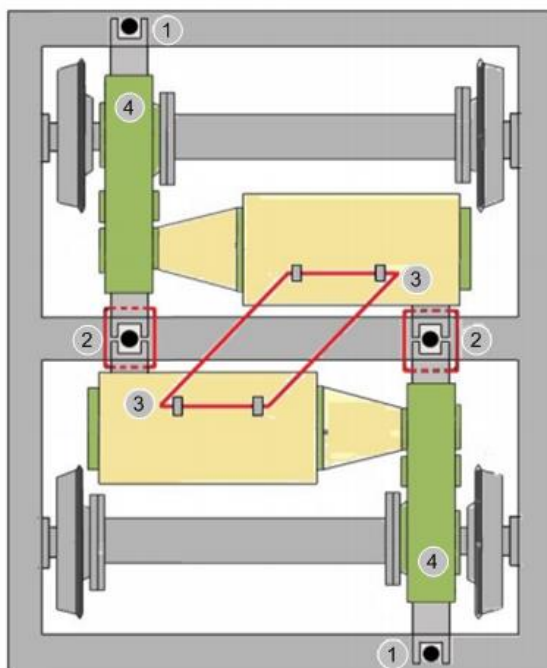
Схема кріплення тягового редуктора: 1 – кріплення через гумометалевий шарнір до кінцевої поперечної балки; 2 – універсальний кронштейн; 3 – тяговий електродвигун; 4 - редуктор
